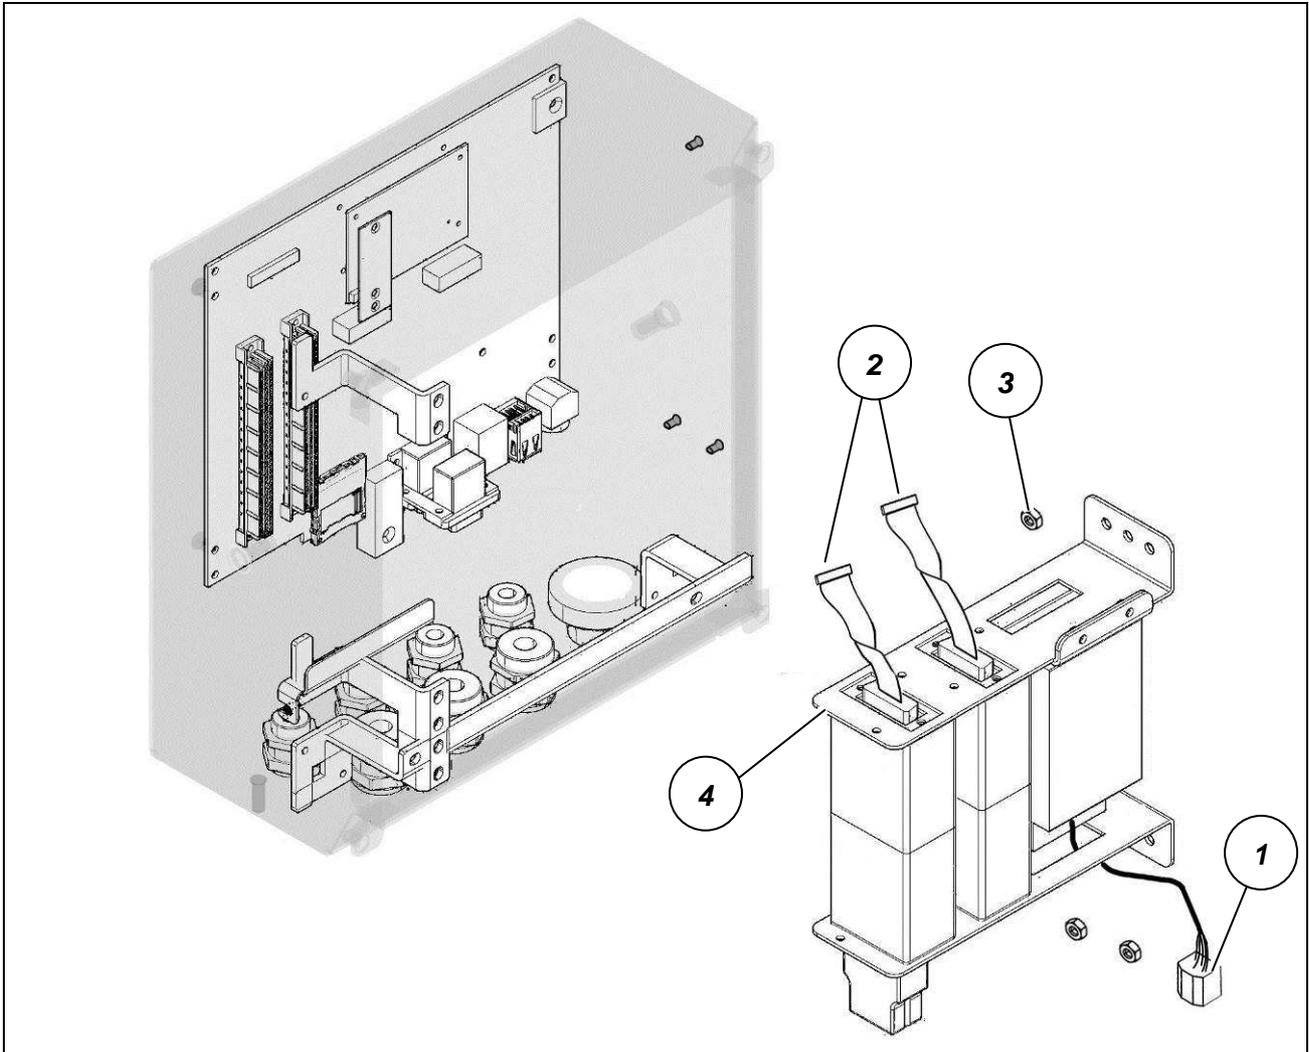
Desmontaje del grupo celdas de pesaje y alimentador terminal
